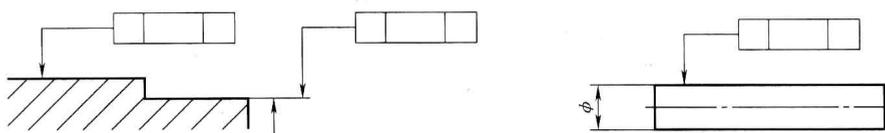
当公差涉及轮廓或表面时几何公差代号的标注
